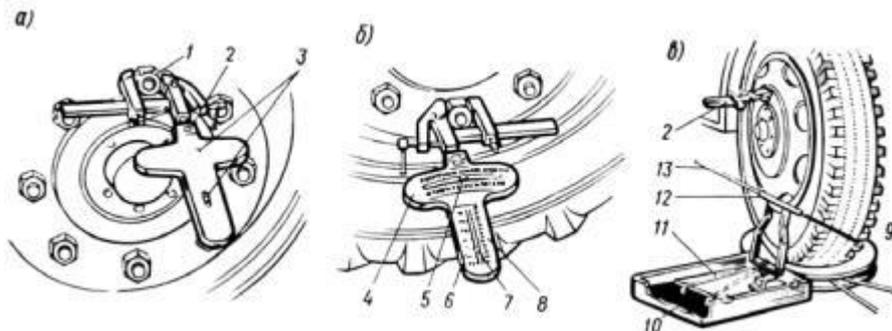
Прибор модели 2183 для измерения углов установки колес автомобиля
